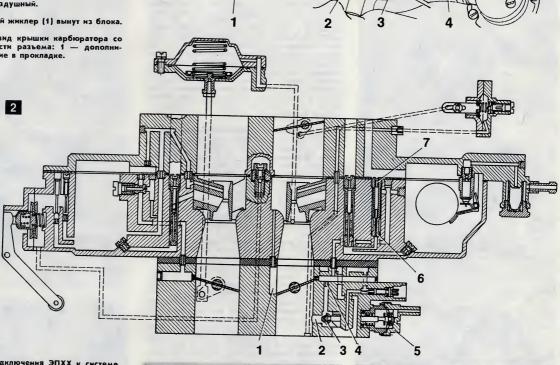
Принципиальная схема карбюратора 2140-1107010: 1 и 2 — воздушный и эмульси-онный каналы автономной системы холостого хода; 3 — клапан ЭПХХ; 4 — байпасный жик-хода; 3 — клапан ЭПХХ; 4 — байпасный жик-лер; 5 — поворотный корпус, регулирую-щий обороты холостого хода; 6 и 7 — топлив-ный и воздушный жиклеры системы холостого хода.
